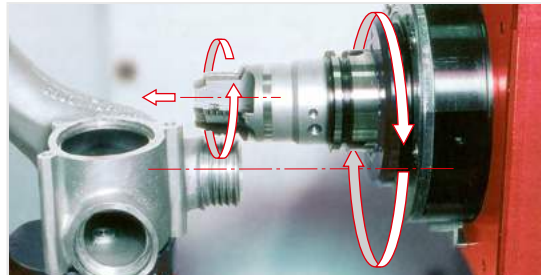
Zirkulargewindefräsen an einem Gehäuse
